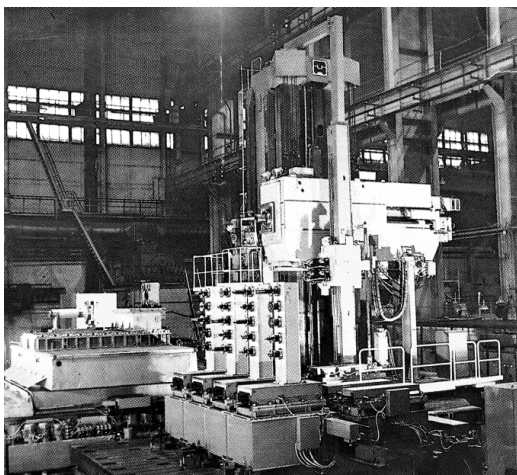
Тяжелый многоцелевой станок сверлильно-фрезерно-расточной группы с поворотным-подвижным столом для обработки корпусных деталей массой до 200 т
